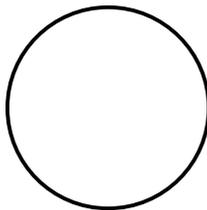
Vista frontal de un autotanque con forma cilíndrica.
